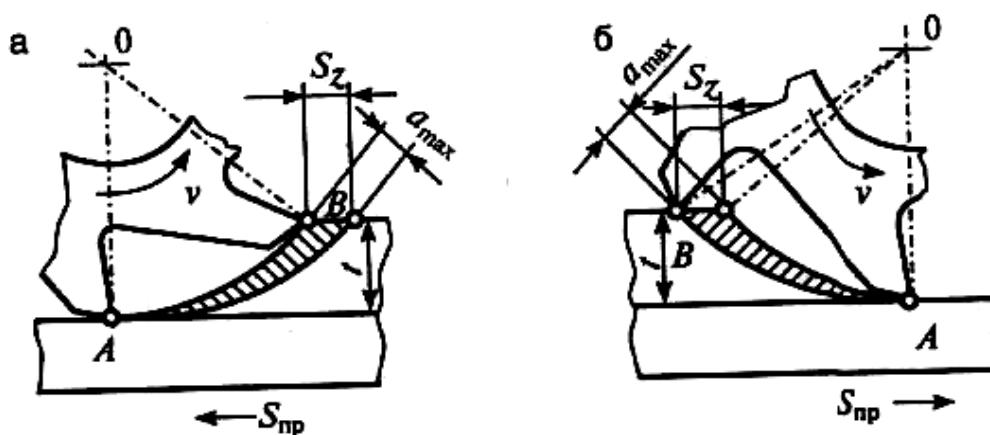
Способы фрезерования: а – встречное; б – попутное
